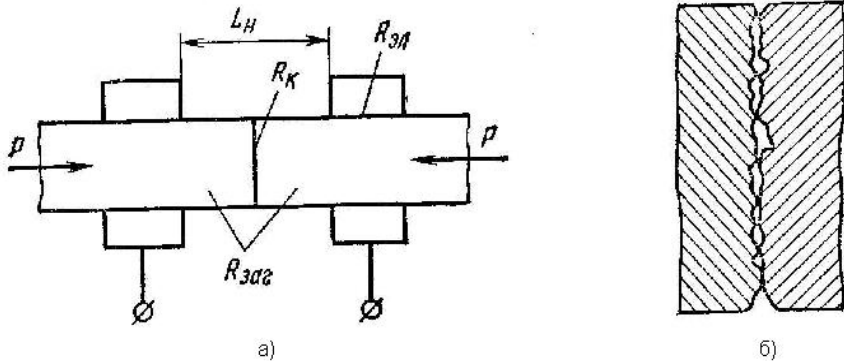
Схема контактной сварки (а) и физического контакта свариваемых деталей
